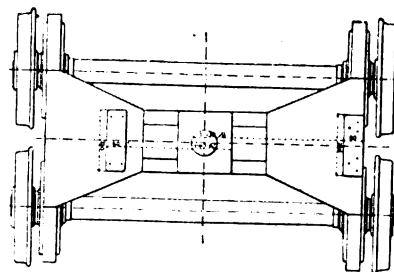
Demi-plan d'un lorry d'avant, demi-plan d'un lorry d'arrière.
